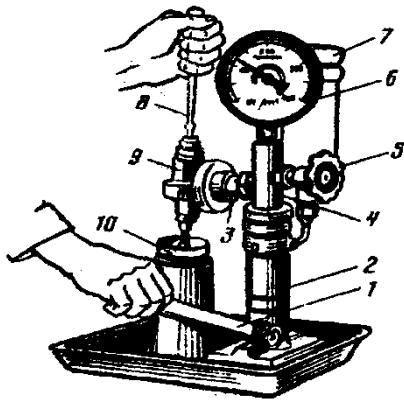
Перевірка і регулювання форсунки на приладі КИ-652: 1 – важіль; 2 – корпус; 3 – маховичок; 4 – розподільник; 5 – запірний вентиль; 6 – манометр; 7 – паливний бачок; 8 – викрутка; 9 – форсунка, що випробовується; 10 – захисний прозорий ковпак
